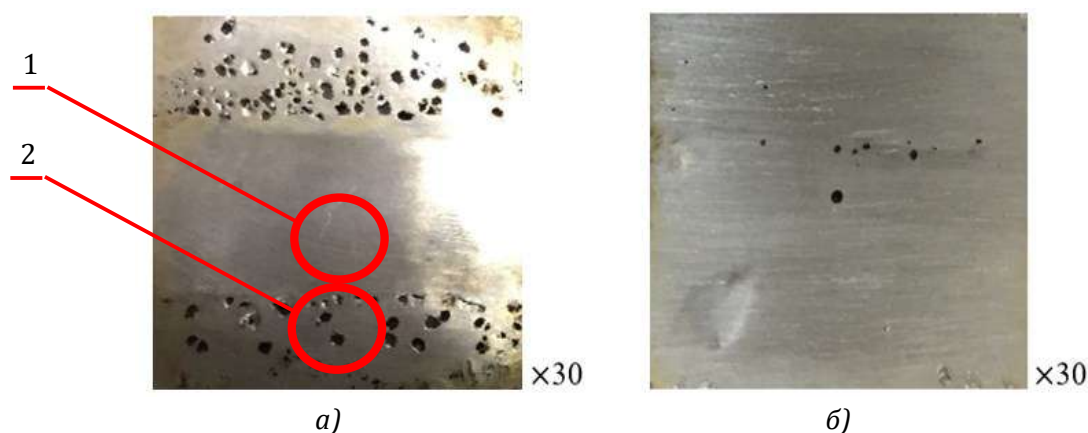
Поверхность сварных швов из СММ с ВП после коррозионных испытаний в растворе хлорида железа (III) (плотность $1,049 \pm 0,002$ г/см³) в течение 216 часов: а – без наплавки; б – с наплавкой в верхнем слое сварочной проволокой ОК Autrod 309L по EN ISO 13749
